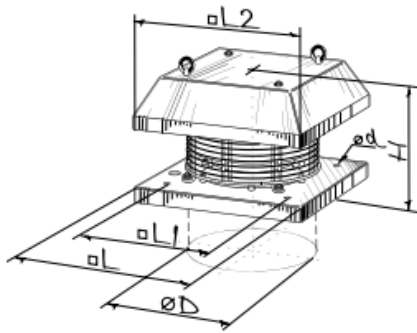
Dimensiones, Líneas Blauberg Axis QR.
